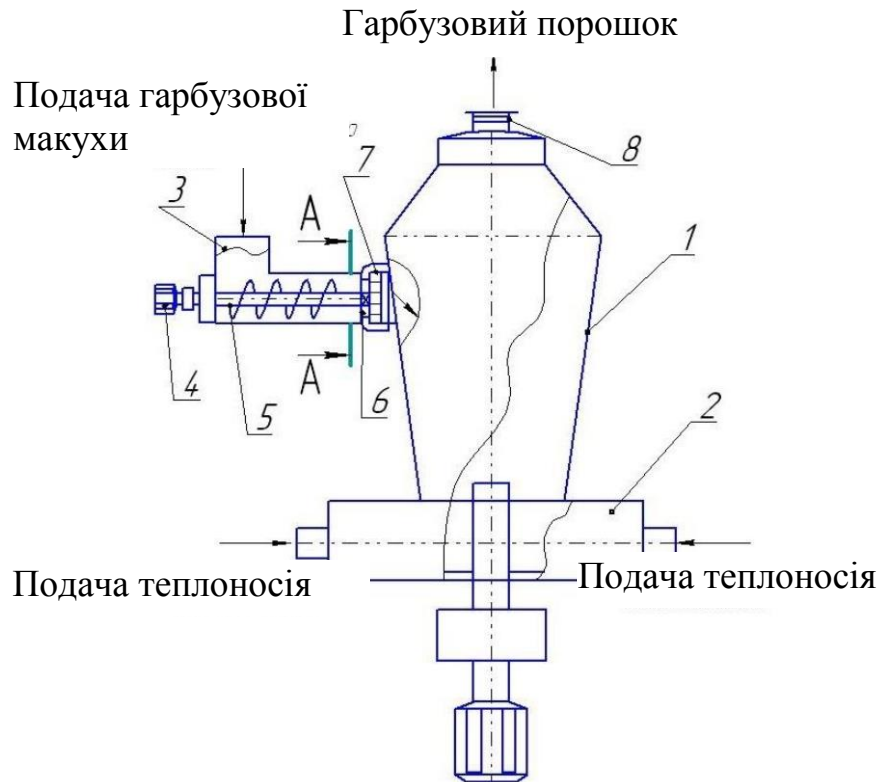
Установка для сушки та подрібнення гарбузової макухи
